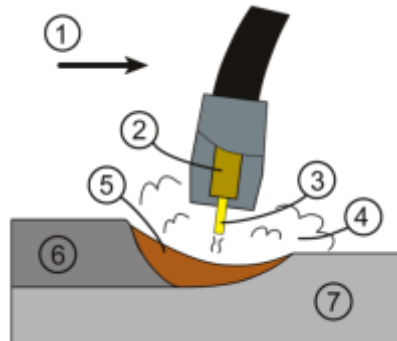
Proceso MIG. 1. Dirección de la soldadura 2. Tubo de contacto 3. Hilo 4. Gas protector 5. Soldadura 6 y 7. Piezas a unir.
